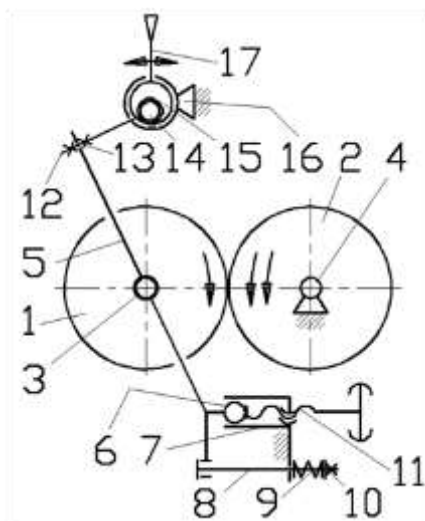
Схема установчого механізму вальцьового верстата.
